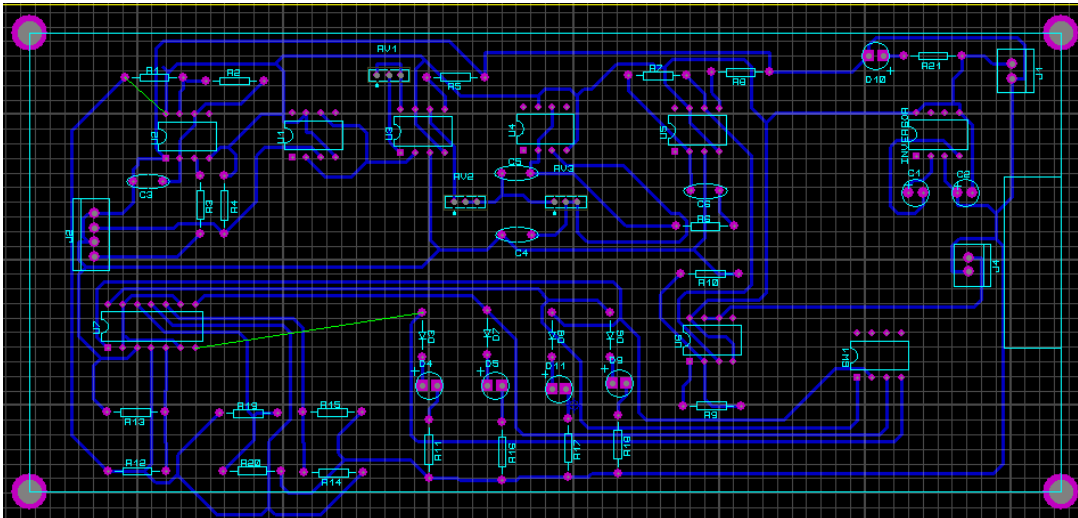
Esquemático del PCB en ARES de la señal Cardíaca.
